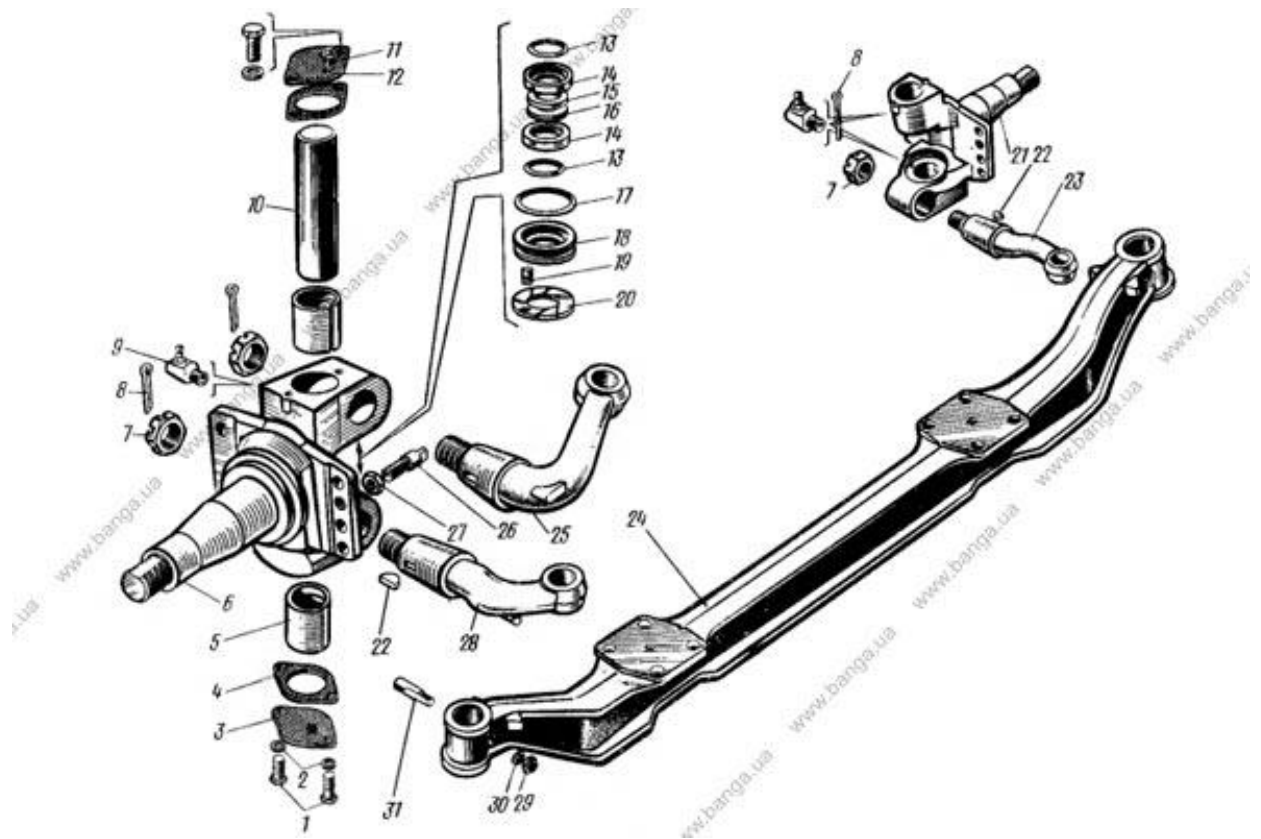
Передня вісь та поворотні кулаки: 1-болт; 2, 30-пружинні шайби; 3-кришка поворотного кулака нижня; 4-прокладка кришки; 5-втулка шворня; 6-кулак поворотної передньої осі лівий; 7, 27, 29-гайки; 8-розвідний шплінт; 9-маслята; 10-шворень; 11-запобіжний клапан; 12-кришка поворотного кулака верхня; 13-ущільнювальне кільце; 14-обойма сальника; 15-шайба кулака; 16-регулювальна шайба; 17-півкільце сальника; 18-кільце опорного підшипника; 19-штифт; 20-шайба опорного підшипника; 21-кулак поворотний правий; 22-сегментна шпонка; 23-важіль поворотного кулака до тяги кермової трапеції правий; 24-балка передньої осі; 25-важіль поворотного кулака до тяги сошки кермового механізму; 26-упор поворотного кулака; 28-важіль поворотного кулака до тяги кермової трапеції; 31-клин шворня
